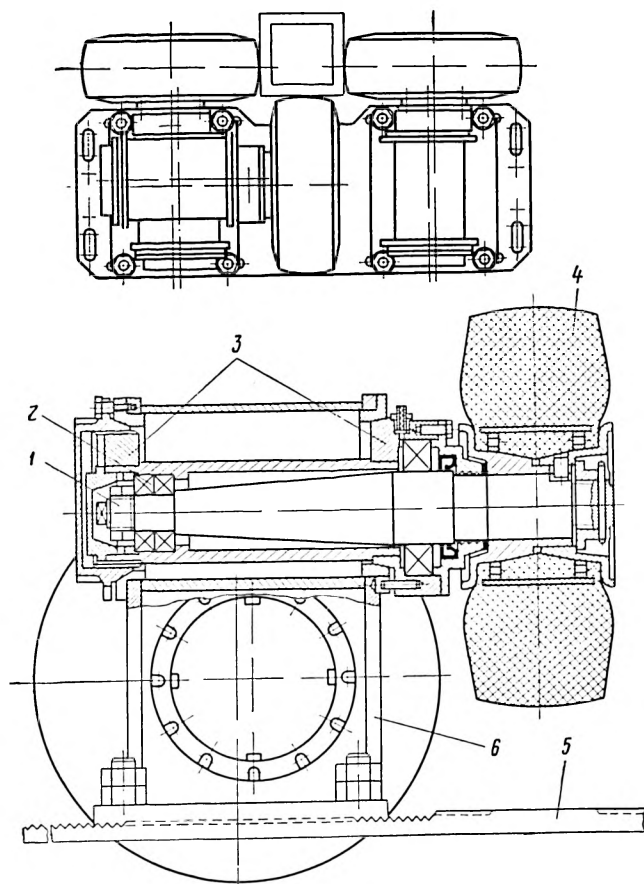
Общий вид блока и разрез роликоопоры конструкции ИГМТК им. М. М. Федорова:
